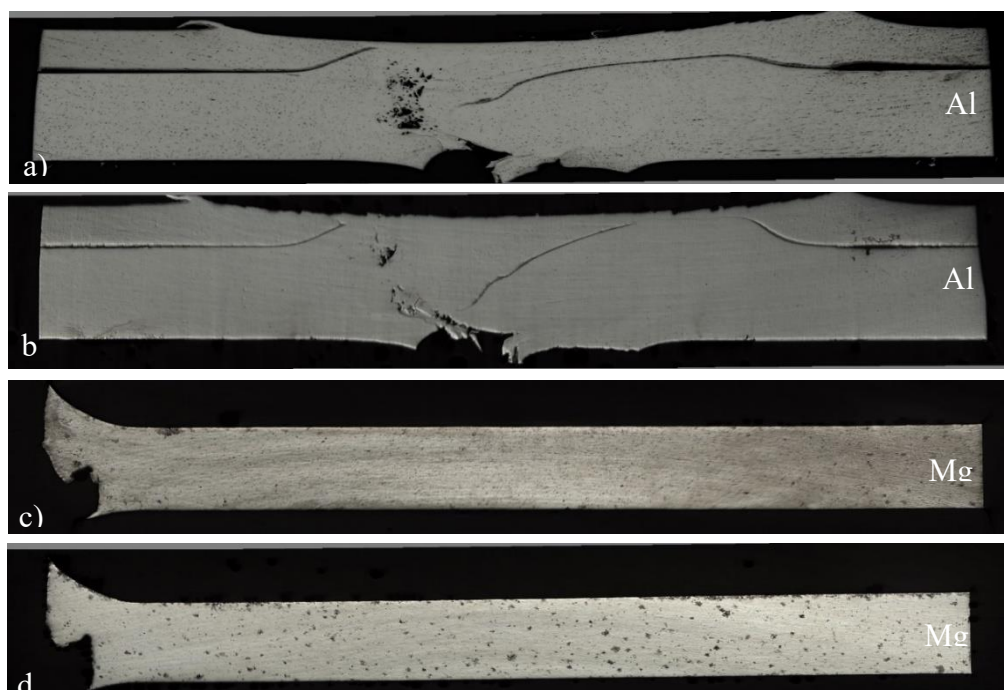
Macroestrutura da secção transversal das soldaduras: a) *skin* da D-870-60-7, b) *skin* da D-870-40-7, c) *stringer* da D-870-60-7 e d) *stringer* da D-870-40-7.
